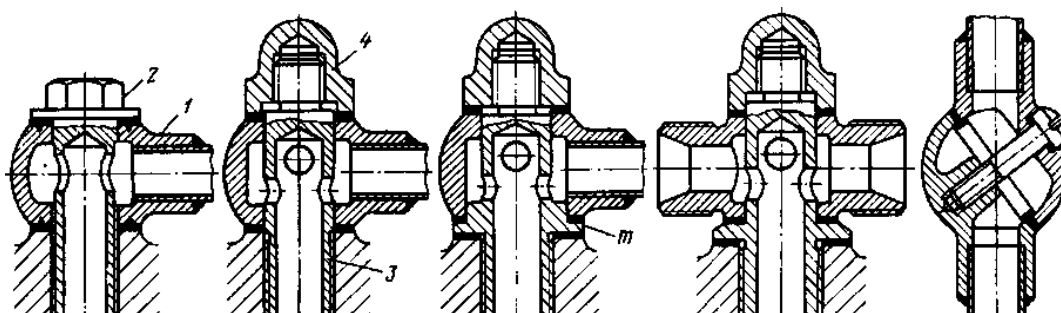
Соединения трубопроводов поворотными ниппелями
